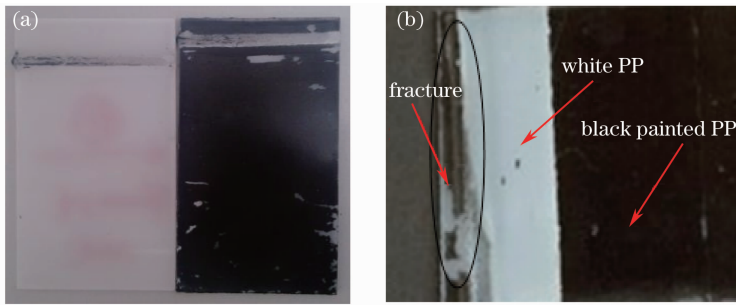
断口形貌图。(a) 断裂在焊缝处; (b) 断裂在接头处
